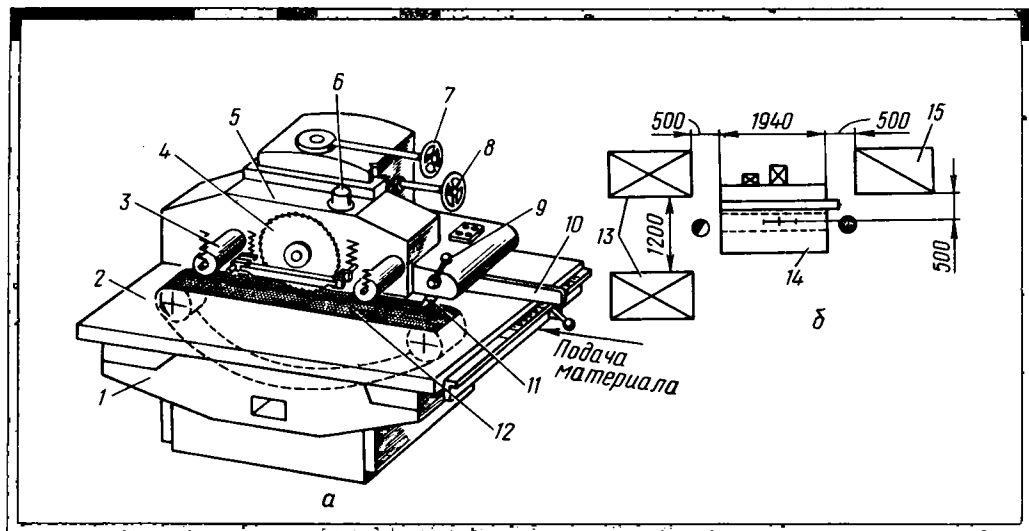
Станок однопильный прирезной с гусеничной подачей ЦДК-5-2:
